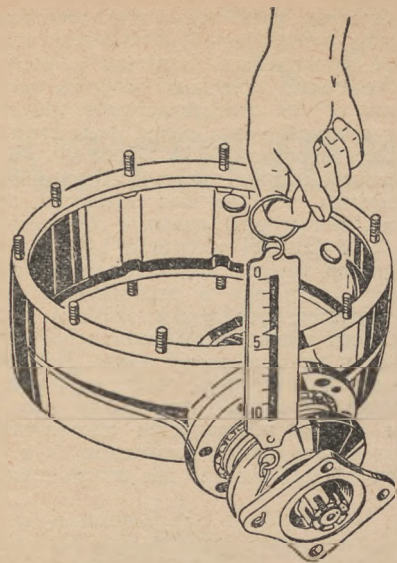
Проверка затяжки подшипников ведущей шестерни.
